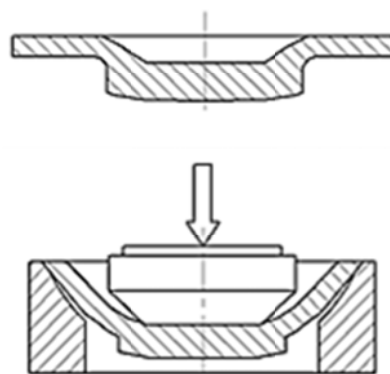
Схема получения поковки дна корпуса реактора вытяжкой в штампе
